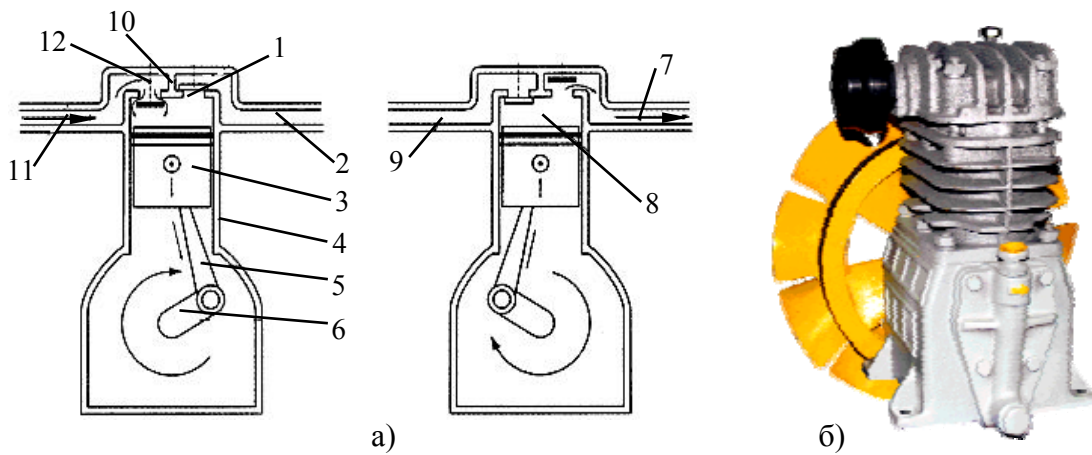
Принцип дії (а) та зовнішній вигляд (б) поршневого компресора: 1, 12 – нагнітальний та всмоктувальний клапани; 2, 7 – нагнітальна лінія; 3 – поршень; 4 – корпус; 5 – шток; 6 – вал; 8 – робоча камера; 9, 11 – всмоктувальна лінія; 10 – перегородка
